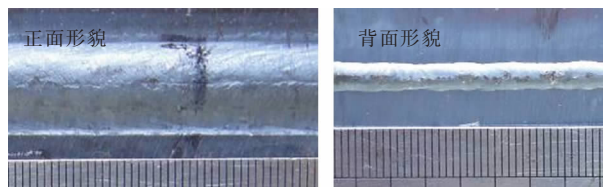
6 mm 厚低碳钢板 DP-TIG 焊接形貌
